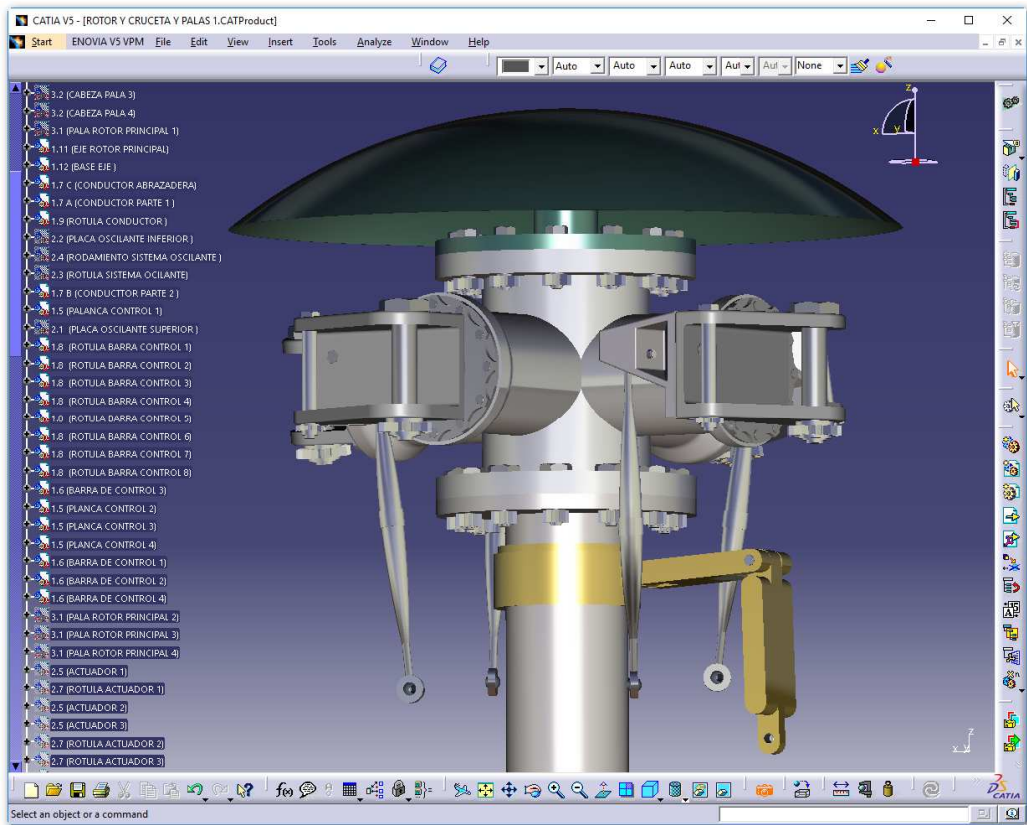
Conjunto cabeza rotor principal - material.
